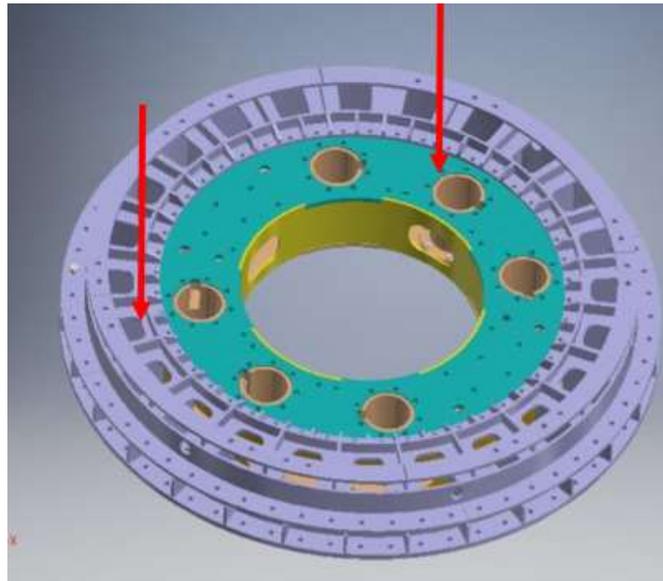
Instalación Filler plate. Tomado de «Instructivo para Montaje de Drive de Espesador de Cuajone» (16 p. 21)
